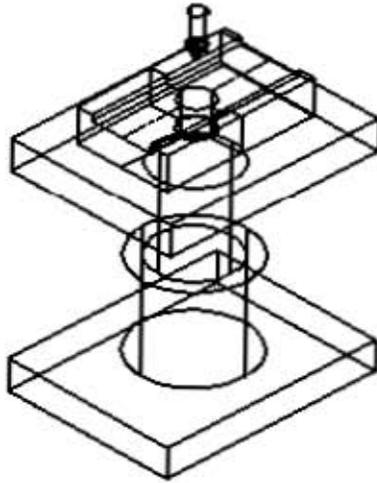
Cuello montado en dispositivo para corte de cuerda.
